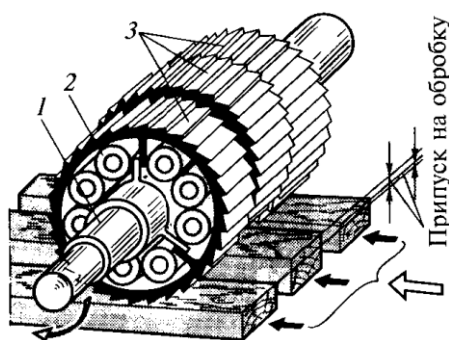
Рифлений секційний валець рейсмусового верстата: 1 – вал; 2 – гумова втулка-амортизатор; 3 – кільця
